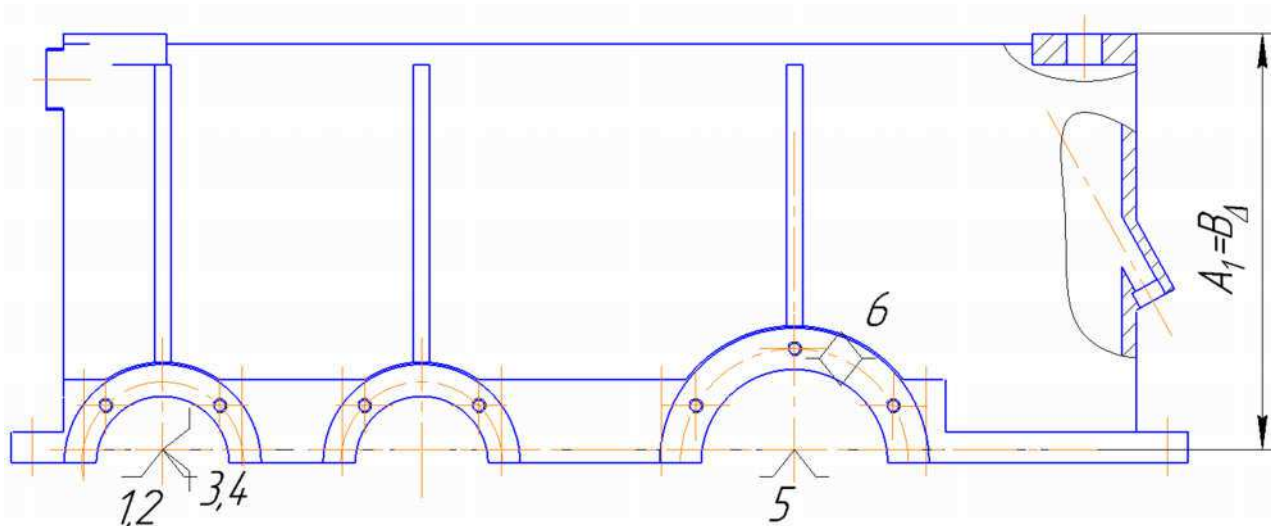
Схема базирования корпуса по осям главных отверстий
